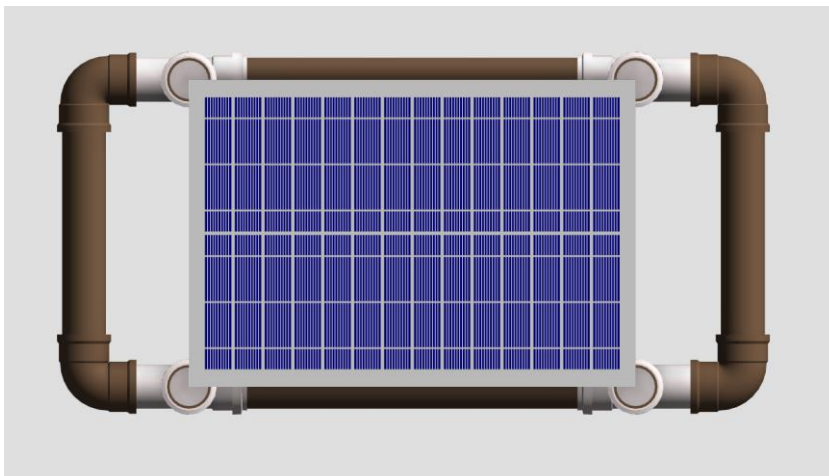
Módulo FV instalado sobre estrutura de PVC.
